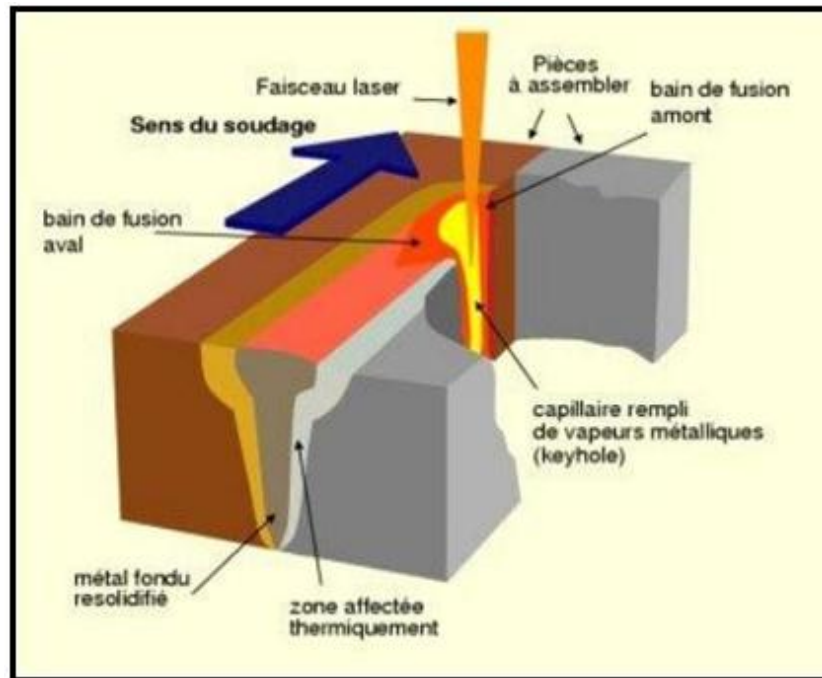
Dispositif typique d'un soudage par laser [9].
